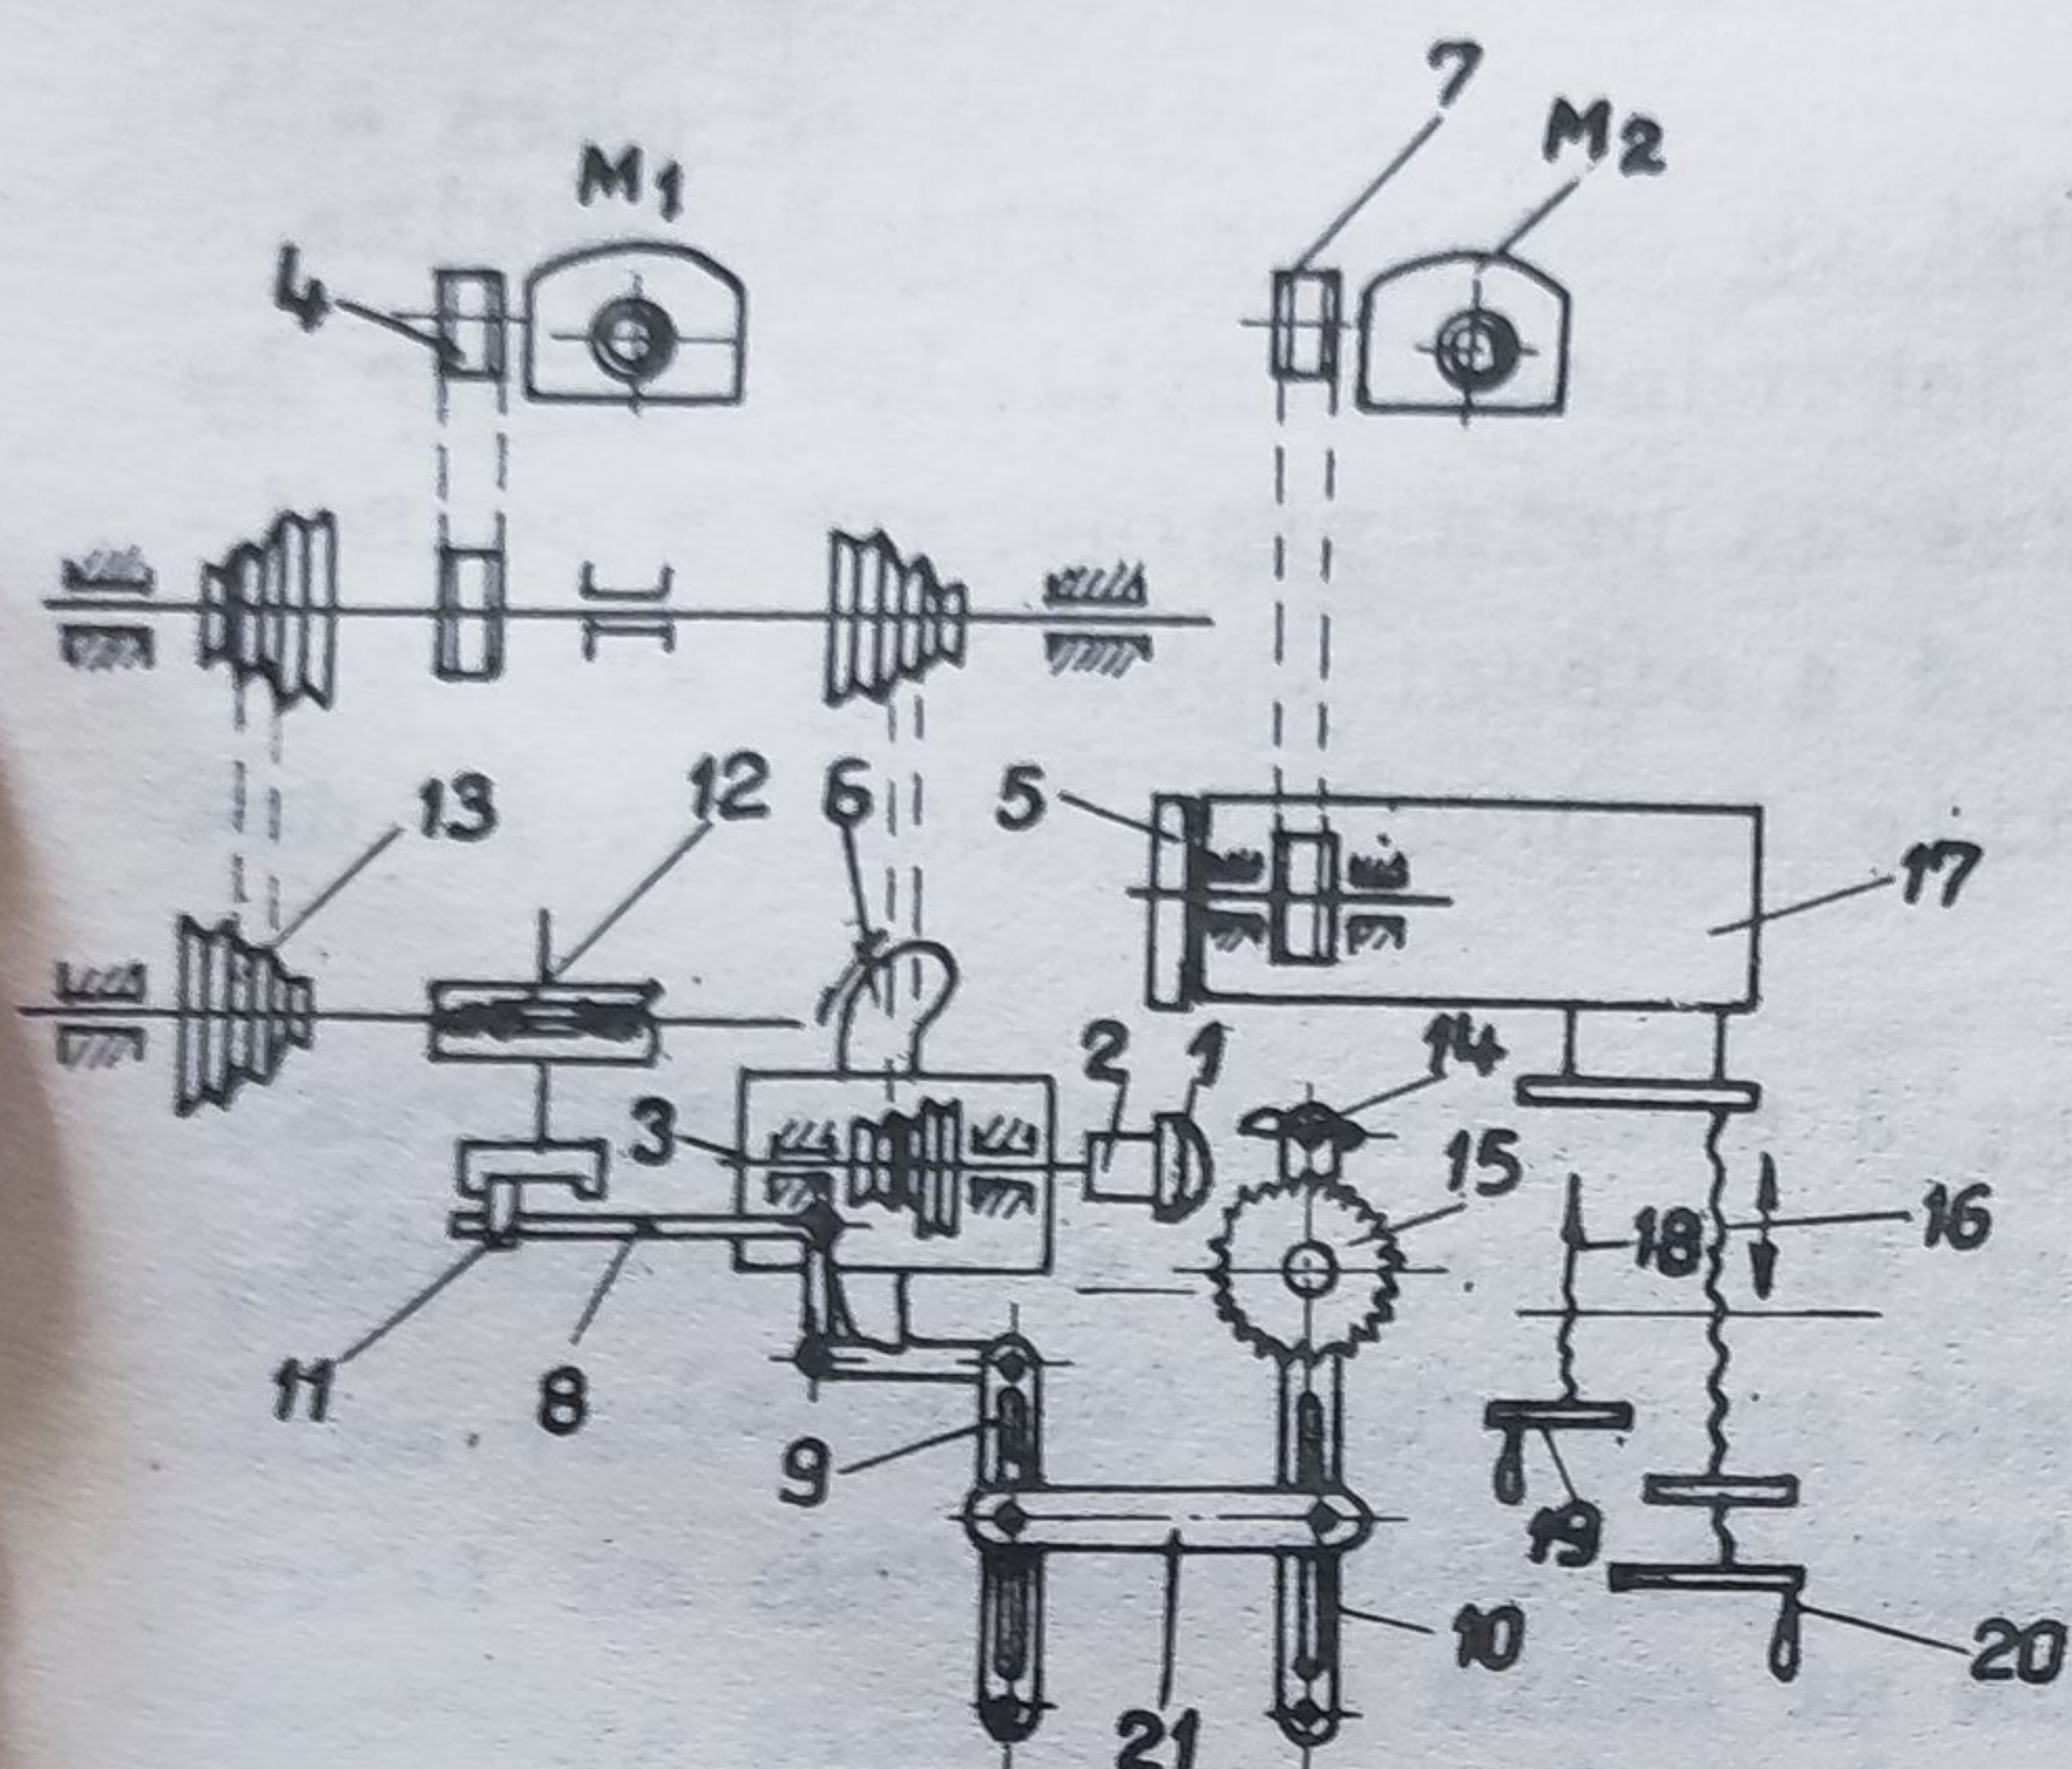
Schema cinematică a mașinii de debordat cu centrare optică.
